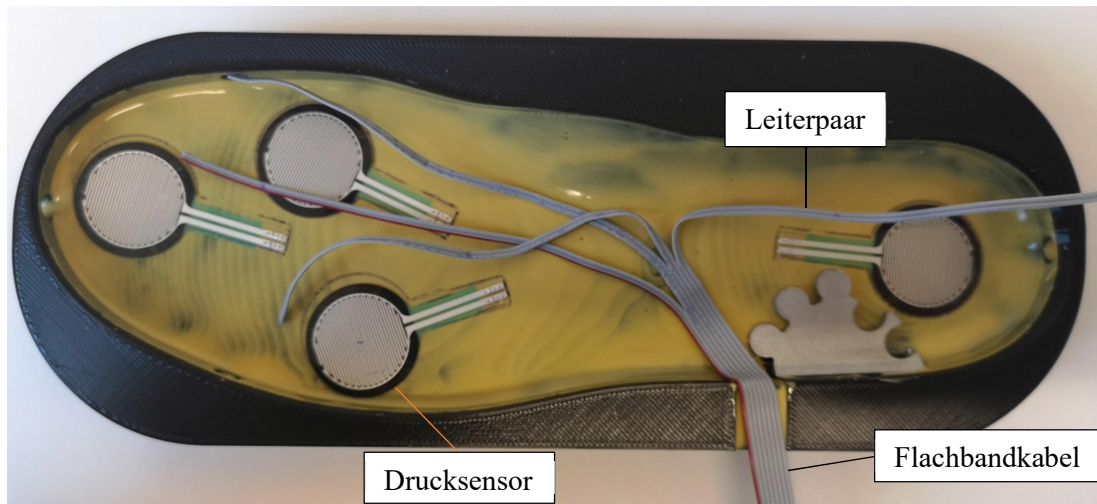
Die eingezeichneten Drucksensoren mit dem Flachbandkabel in der unteren Gussform
